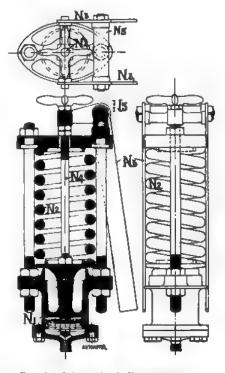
Schnitt durch Excenterpumpe, rechts: Ansicht; oben: Grundriss.
